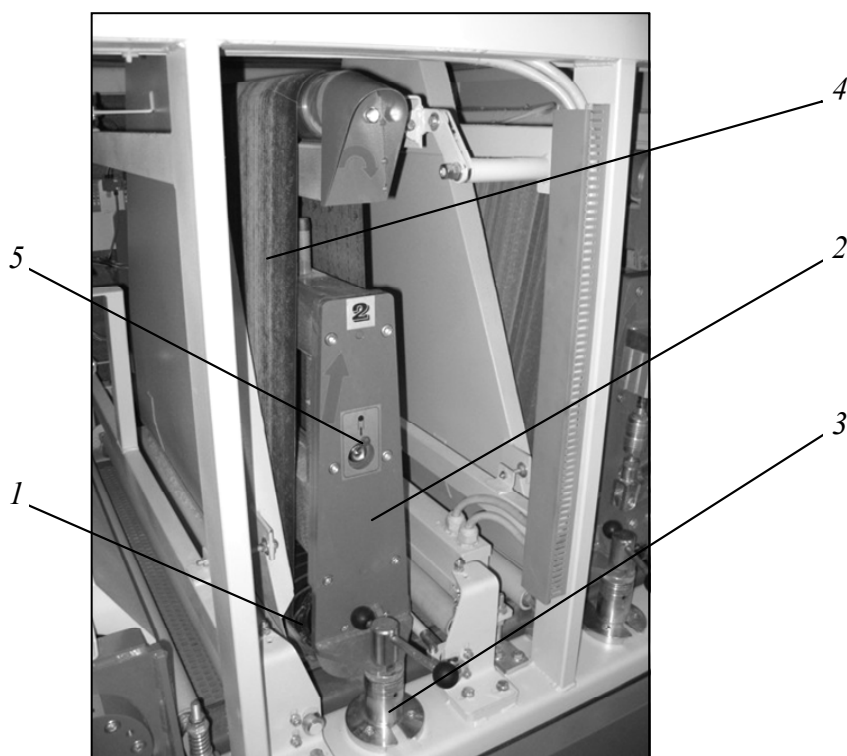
Калибровальный узел *R* широколенточного фрезерно-шлифовального станка Houfek Bulldog FRC 910
